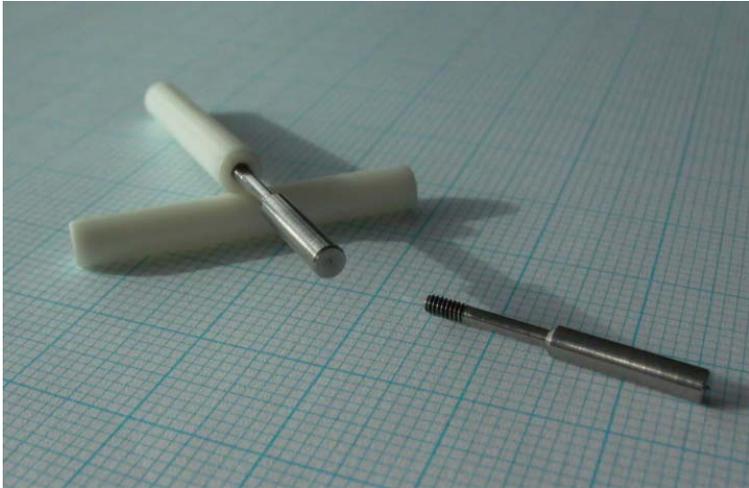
Gewindehülse in ZrO_2 mit Innengewinde M 1,6
